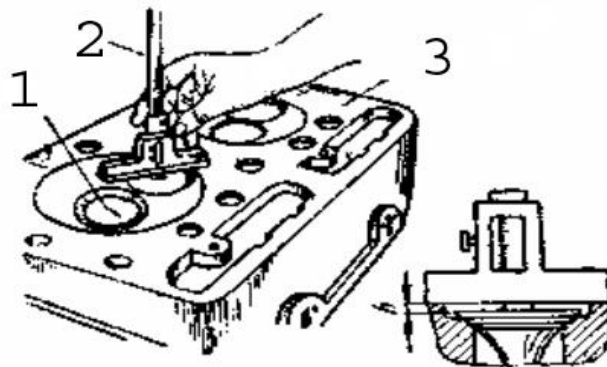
Вимірювання глибини заглиблення клапана: 1 - клапан; 2 - штангенглибиномір; 3 - головка блока
